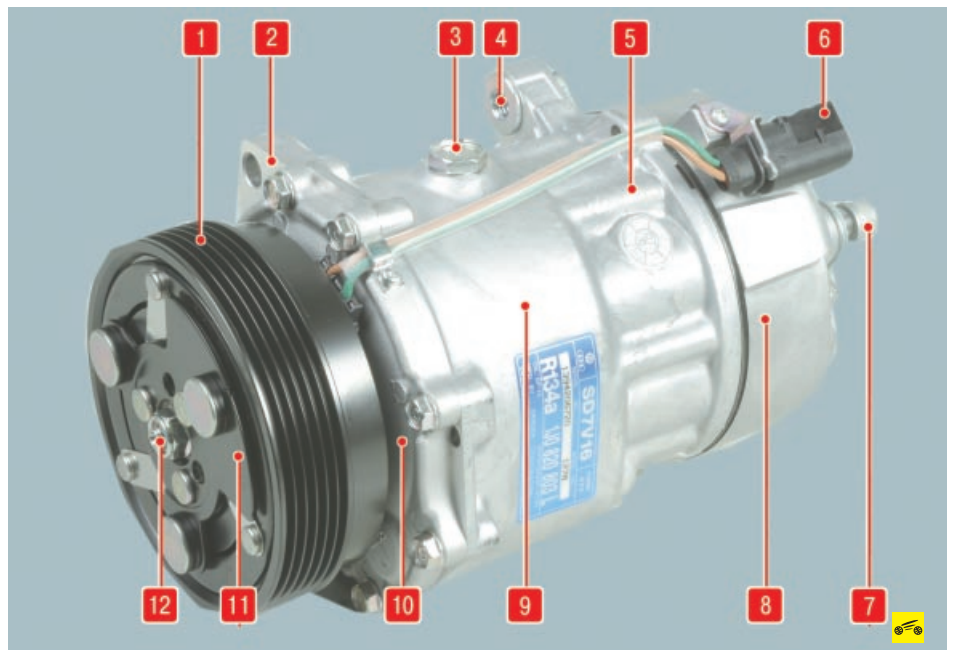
Компрессор кондиционера: 1 – шкив привода; 2 – передняя проушина крепления; 3 – пробка заливки масла; 4 – задняя проушина крепления; 5 – блока лепестковых клапанов; 6 – колодка разъема жгута проводов; 7 – болт крепления фланца трубопровода; 8 – крышка блока клапанов; 9 – корпус компрессора; 10 – передняя крышка корпуса; 11 – прижимная пластина; 12 – гайка крепления прижимной пластины
